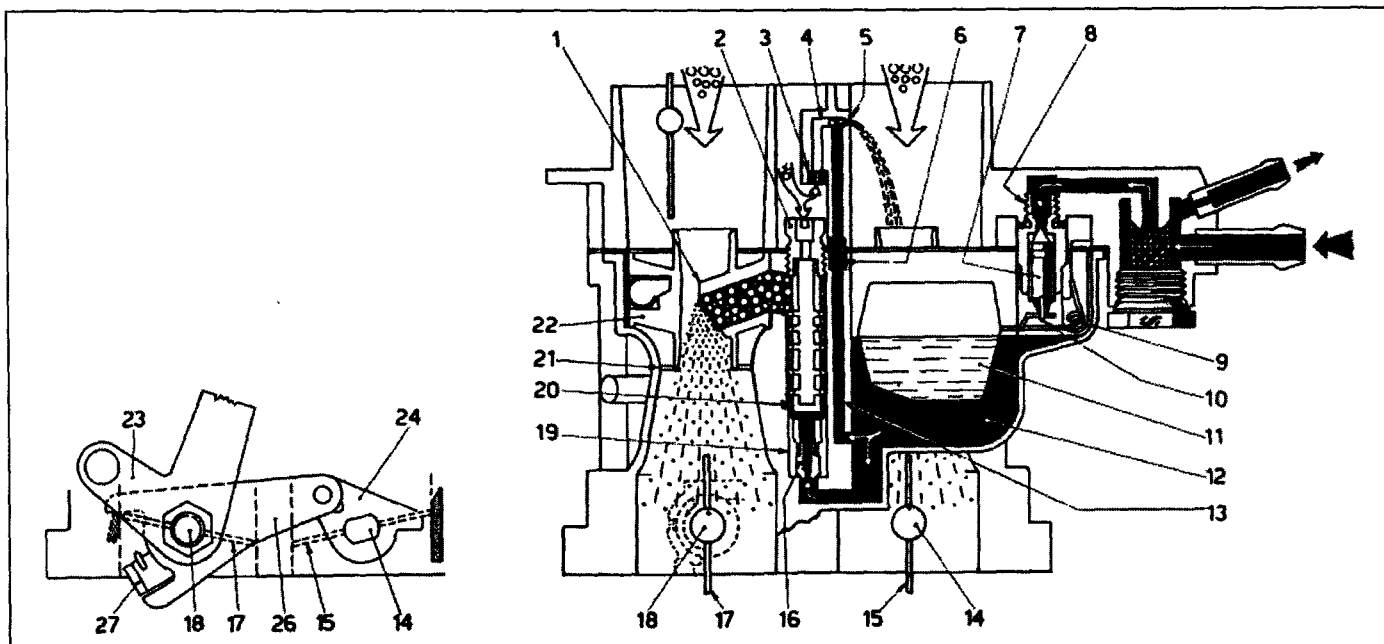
Поплавковая камера, главная дозирующая система и система обогащения "полных нагрузок"
